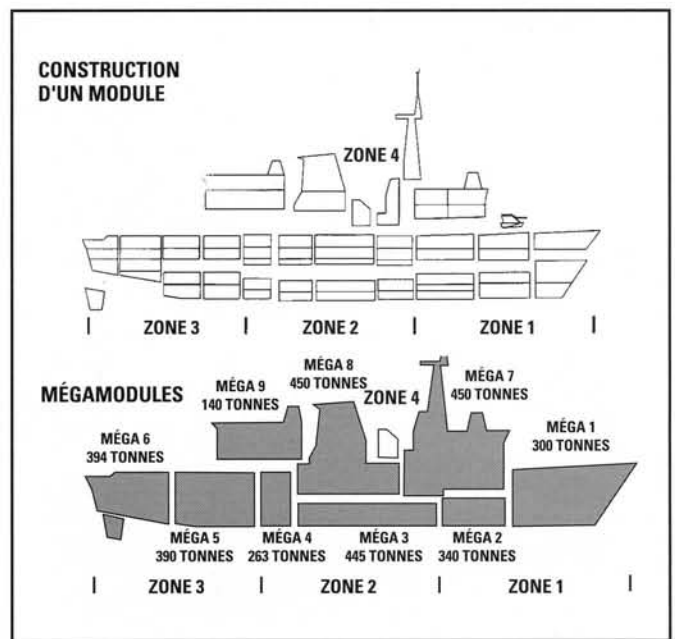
Construction par mégamodules par rapport à la construction par modules.
